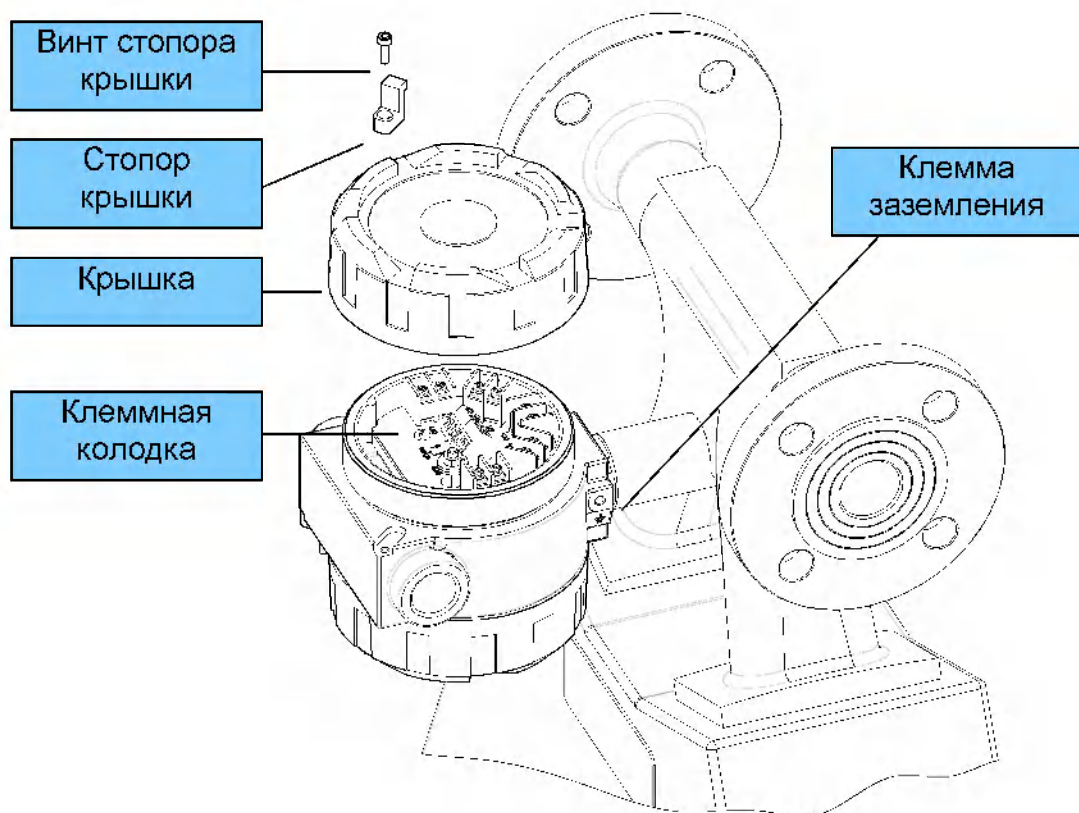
Корпус измерительного модуля (исполнения И, В) или клеммной коробки (исполнения Р, РВ), размещенный на датчике.
